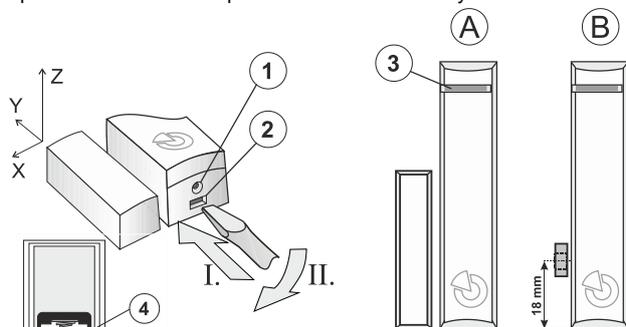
отверстие для стопорного винта, 2 - выступ корпуса, 3 - светодиодный индикатор, 4 - батарея, 5 - серийный номер, 6 - контакт для вскрытия корпуса
